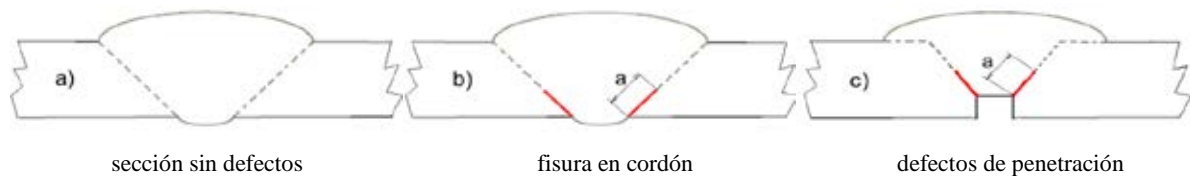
Posicionamiento de fisuras en modelos de la sección transversal
